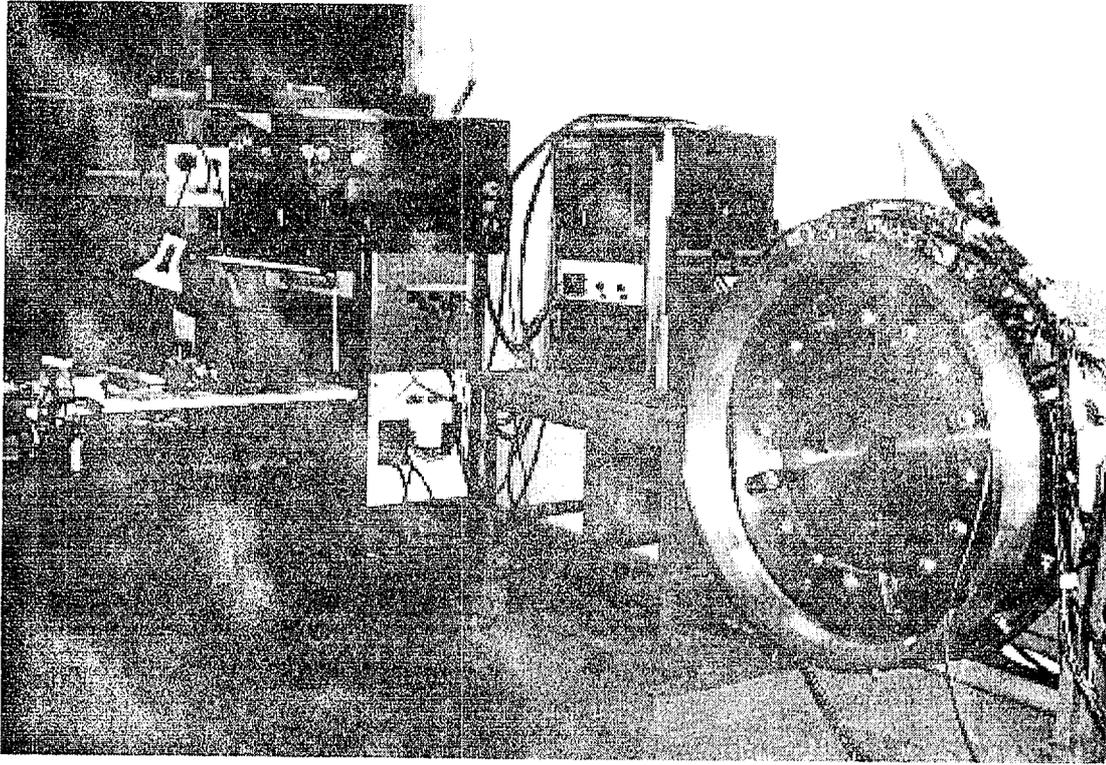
, Cabecal de soldadura de caños, desarrollo de procedimientos.
